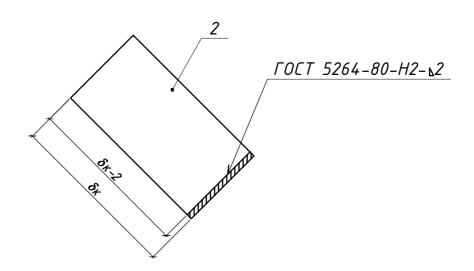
Бандаж стяжной (для вертикальных трубопроводов dн от 45 до 159 мм)
